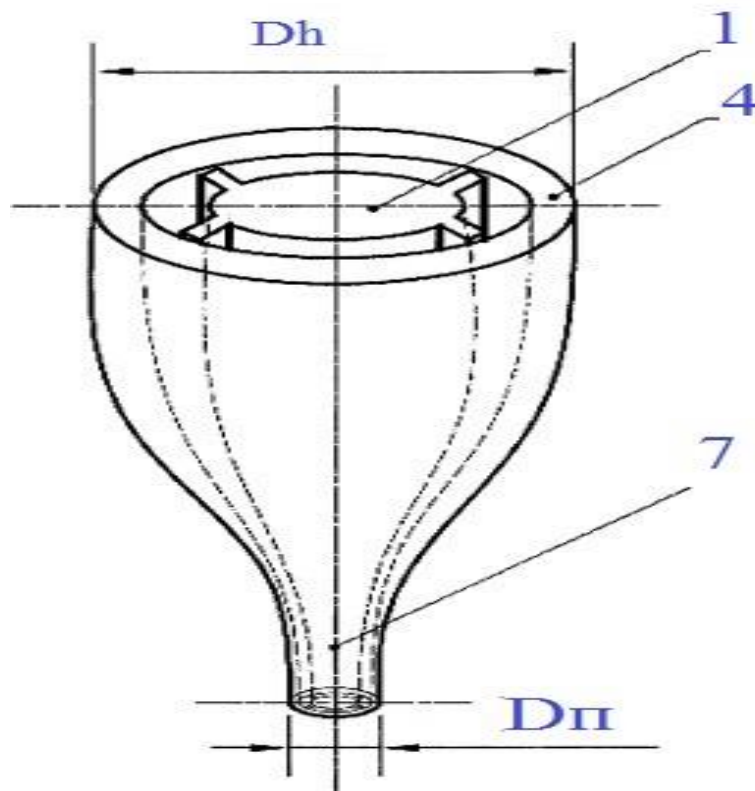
Схема перетяжки стержня заготовки с кварцевой трубой в предзаготовку
